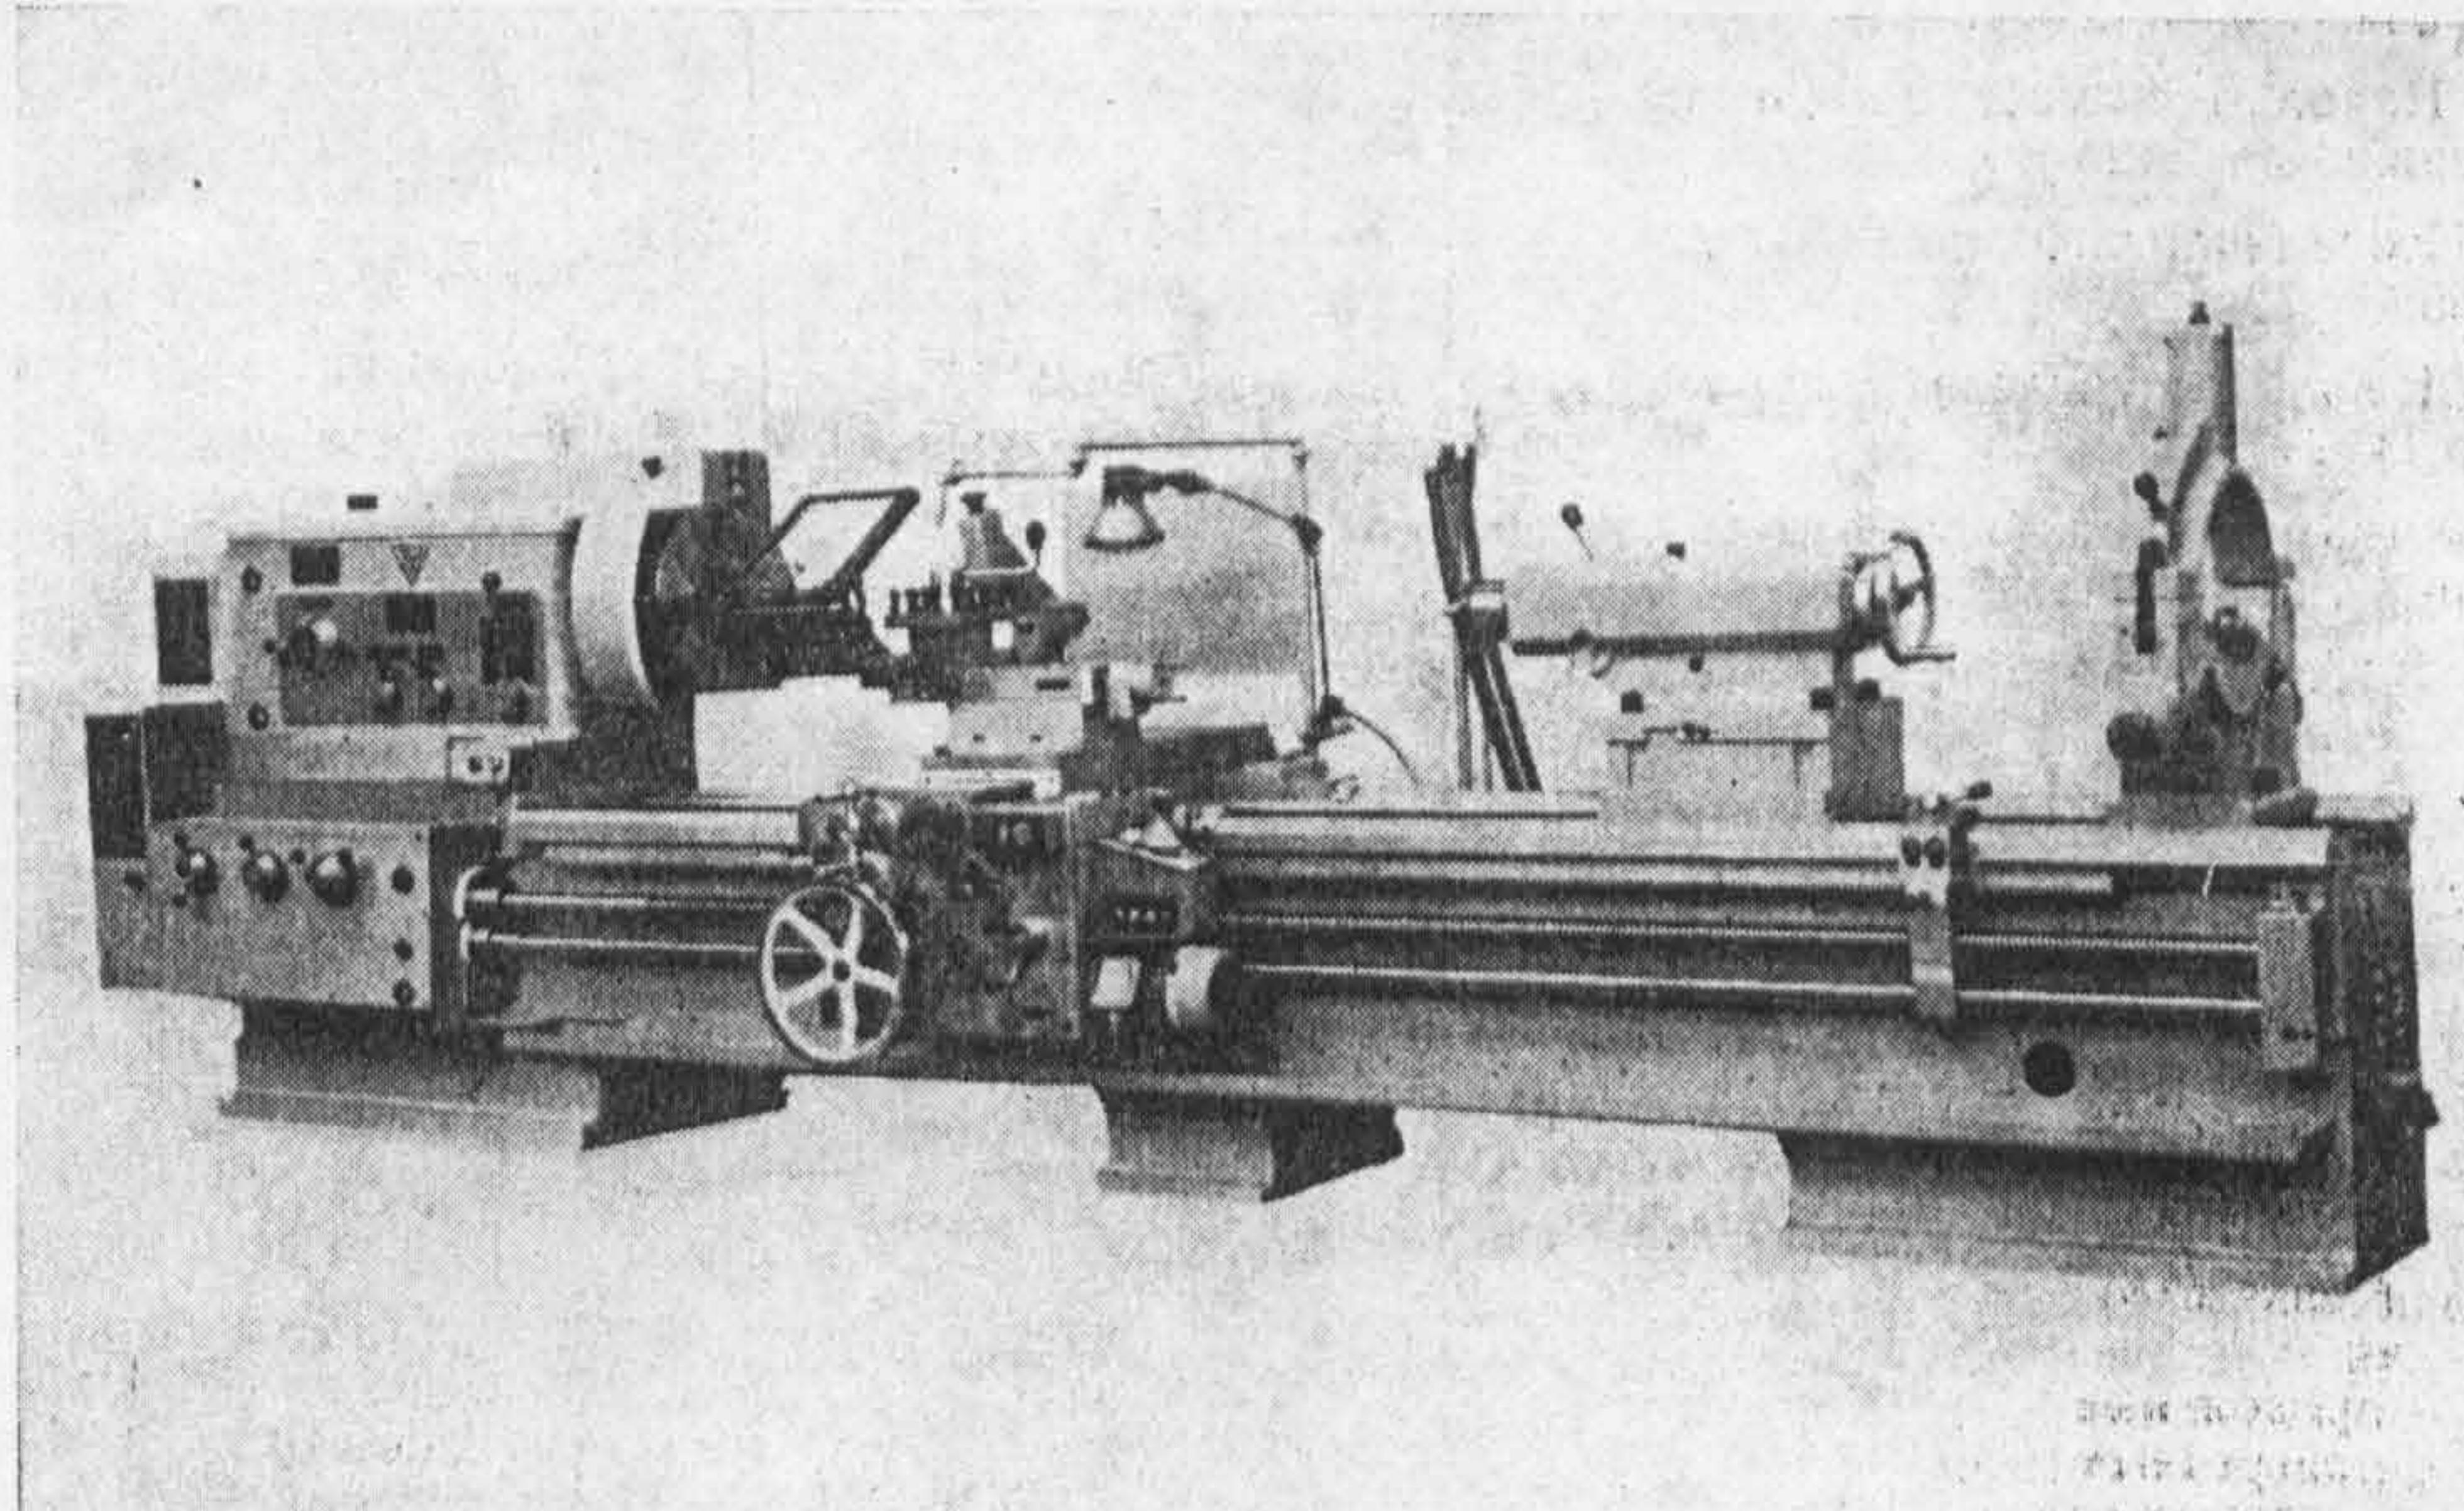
Общий вид токарно-винторезного станка мод. 16К40.
